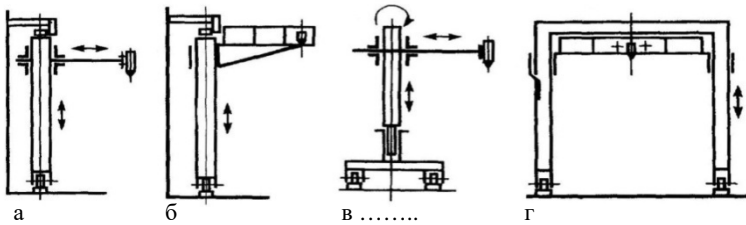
Тележки для сварочных аппаратов:
